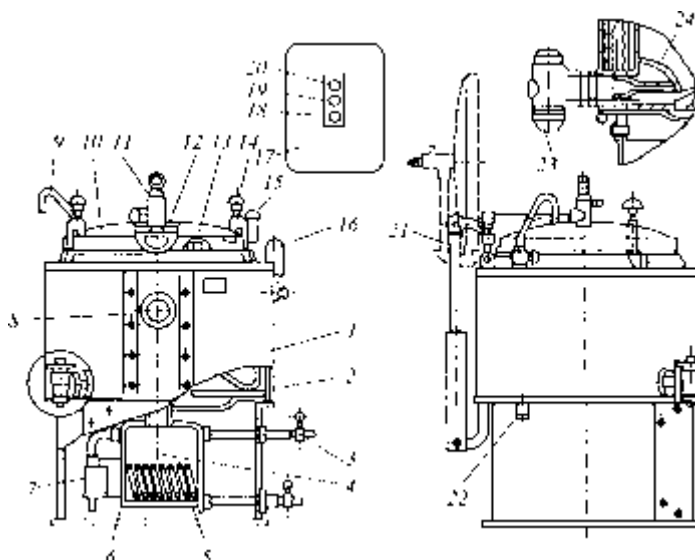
Котел пищеварочный электрический КПЭ-100/1 - облицовка; 2 - теплоизоляция; 3 - пробноспускной кран; 4 - датчик; 5 - тэны; 6 - парогенератор; 7 - реледавления; 8-манометр; 9-поворотныйкран; 10-крышка; 11 -клапан-турбинка; 12-отражатель клапана-турбинки; 13 - прокладка; 14 - накладные рычаги; 15 -воронка; 16-двойнойпредохранительныйклапан; 17-станцияуправления; 18-ручка; 19-лампа «Включено»; 20-лампа«Нетводы»; 21-противовес; 22-трубопроводхолоднойводы; 23-сливной кран; 24-фильтр
